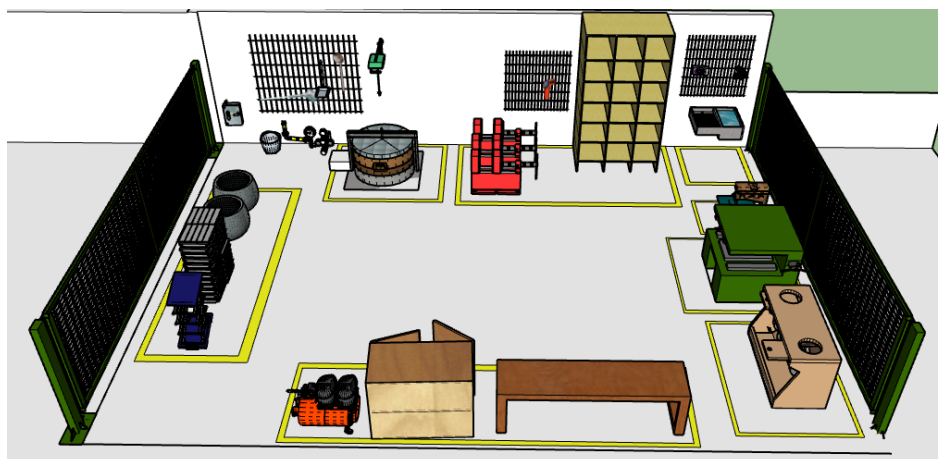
Propuesta Diseño de Planta Vista Lateral. Fuente: Elaboración propia.
